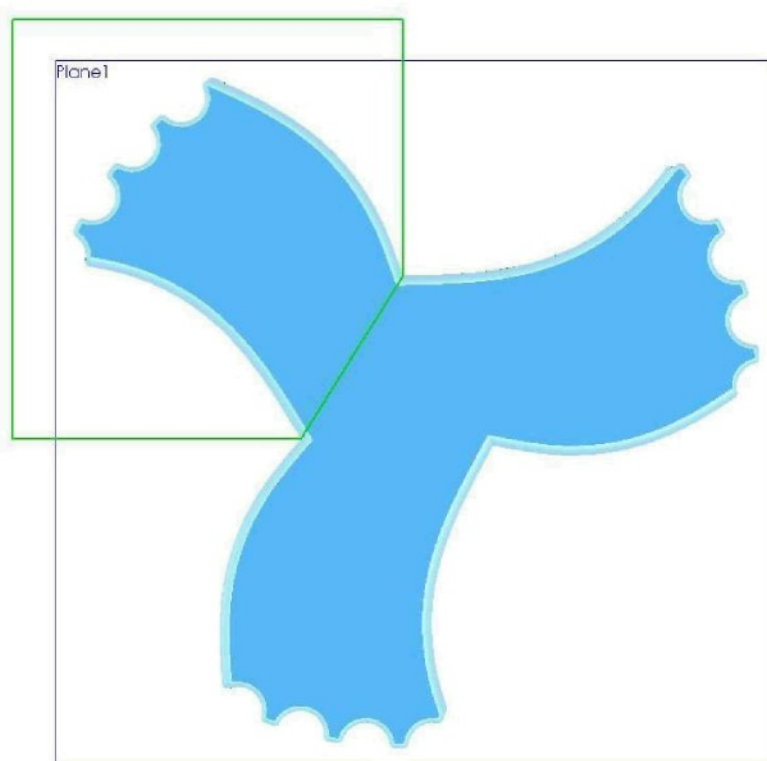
Převodník základní tvar, upravený počet zubů
